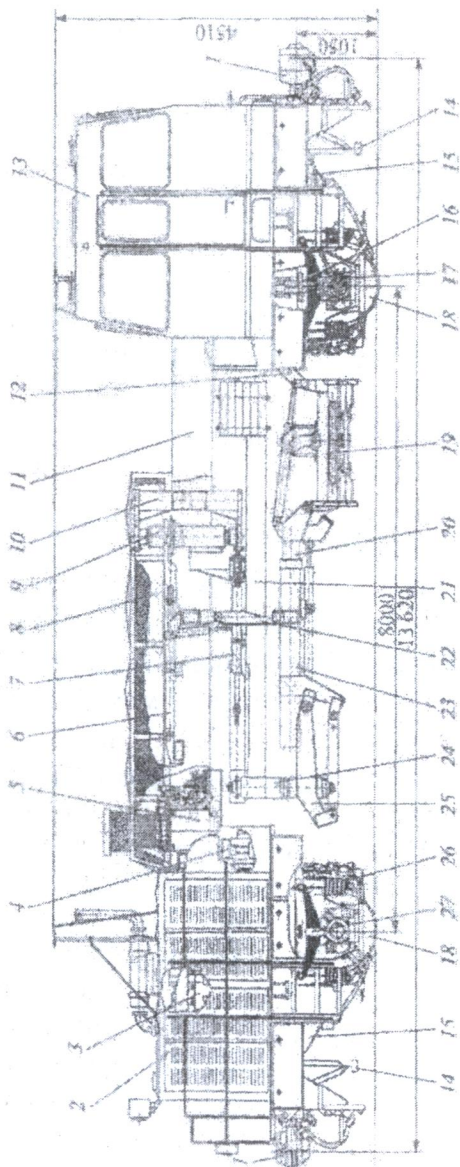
Общий вид кустореза СП-93Р: 1 – автосцепка; 2 – капот; 3 – дизель-генератор; 4 – компрессор; 5 – насосная станция; 6 и 7 – механизмы поворота верхнего и нижнего плеча; 8 – укрытие; 9 и 24 – опоры механизма поворота верхнего и нижнего плеча; 10 – опора верхнего плеча; 11 – рама; 12, 22 – крью запорный ротора-фрезы и нижнего плеча; 13 – кабина; 14 – приемные катушки АЛСН; 15 – песочница; 16 – арретир; 17 – привод скоростемера; 18 – колесно-моторный блок; 19 – ротор-фреза с механизмами привода; 20 – телескопическая балка; 21 – верхнее плечо с противовесом; 23 – нижнее плечо с выдвинутой балкой; 25 – кронштейн нижнего плеча с приводом; 26 – тормозная рычажная передача; 27 – рессорное подвешивание
